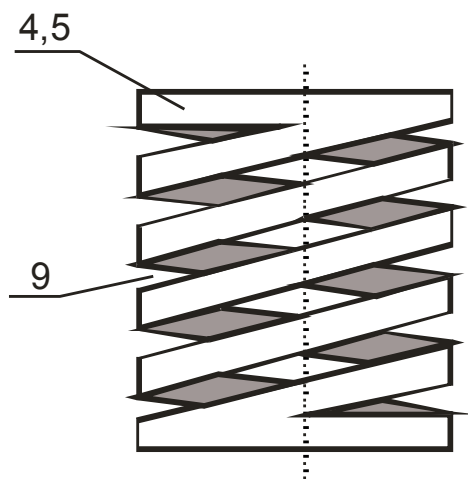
Плавающая опорная втулка (подшипник скольжения)
